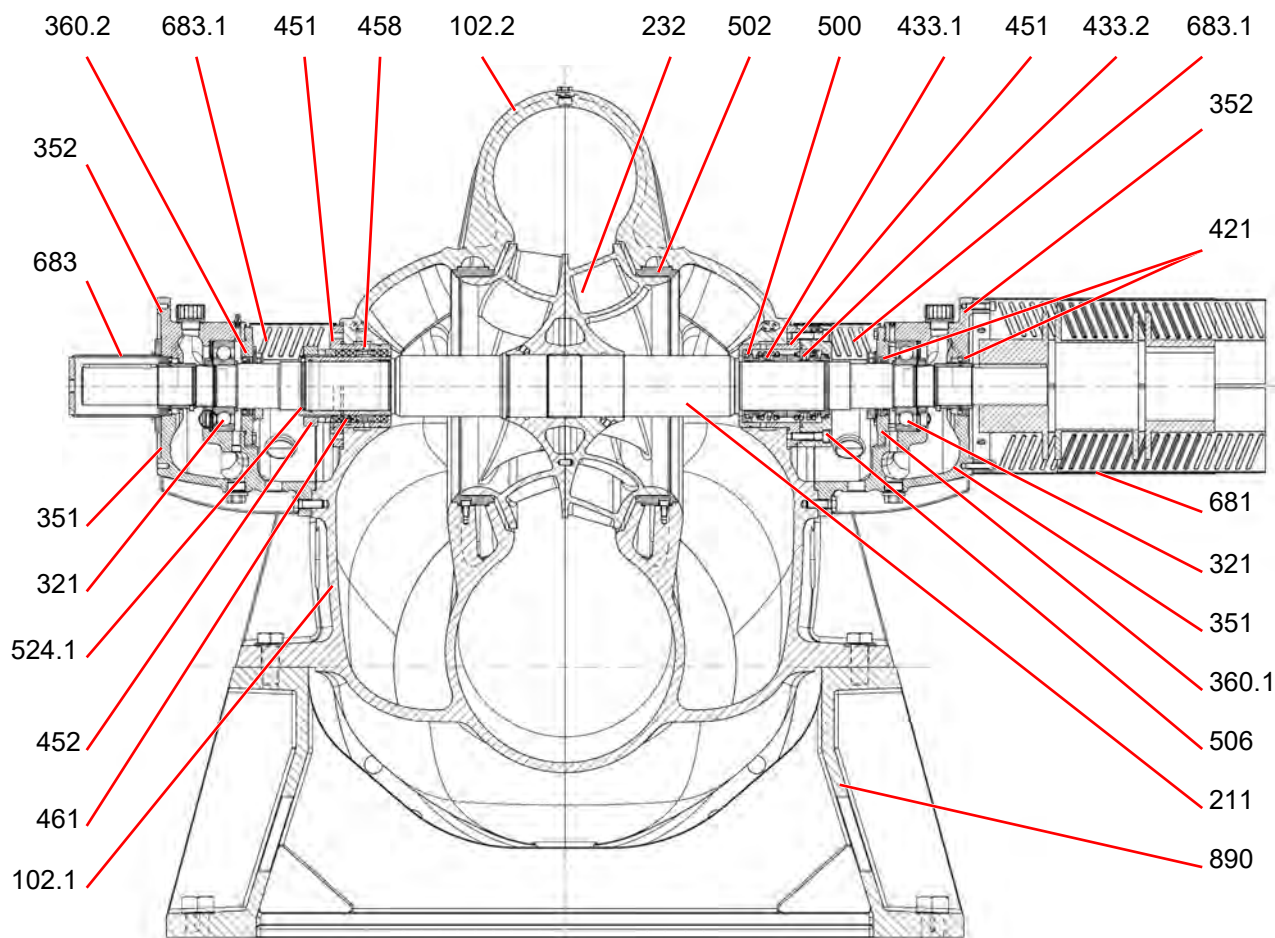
Чертеж насоса ASP-R.P.S в разрезе (соосные лопасти рабочего колеса, платформа, прессовая посадка)
